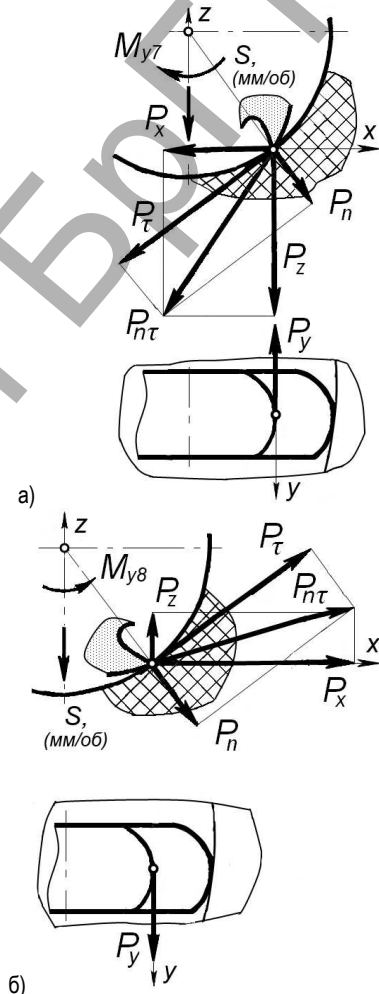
Схемы действия составляющих силы резания со стороны дисковых фрез на поверхность отверстия: а – дисковой фрезы 7; б – дисковой фрезы 8
